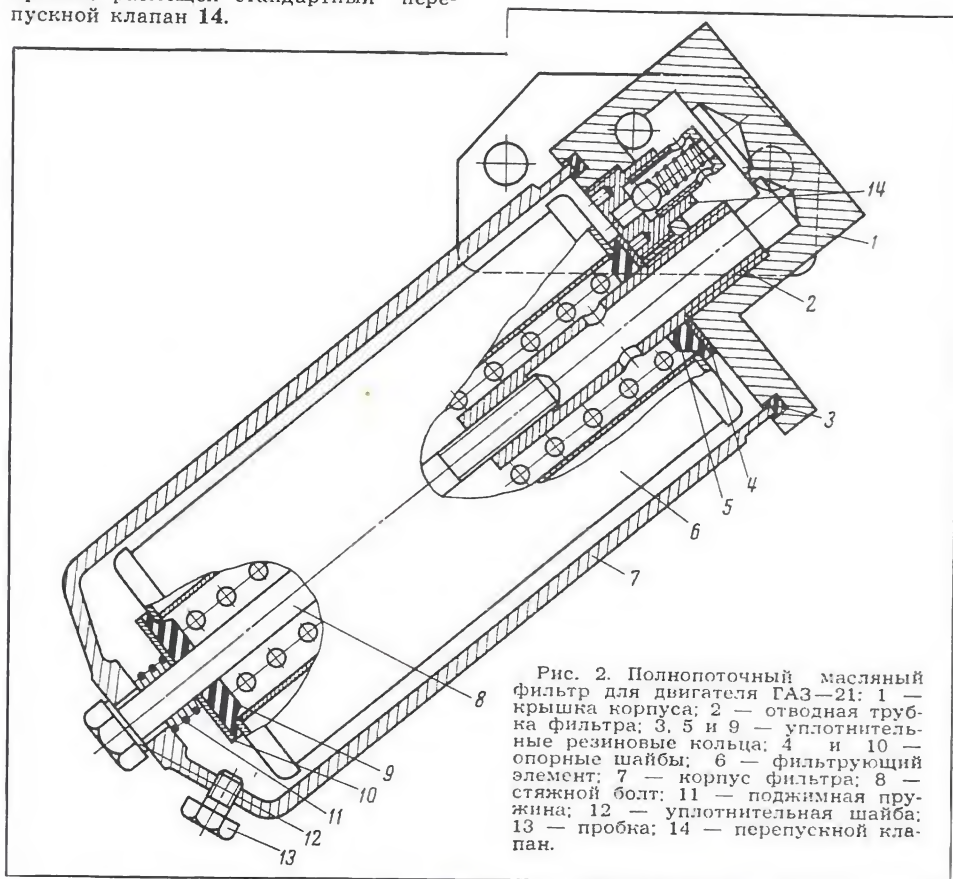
Полнопоточный масляный фильтр для двигателя ГАЗ—21: 1 — крышка корпуса; 2 — отводная трубка фильтра; 3, 5 и 9 — уплотнительные резиновые кольца; 4 и 10 — опорные шайбы; 6 — фильтрующий элемент; 7 — корпус фильтра; 8 — стяжной болт; 11 — поджимная пружина; 12 — уплотнительная шайба; 13 — пробка; 14 — перепускной клапан.
